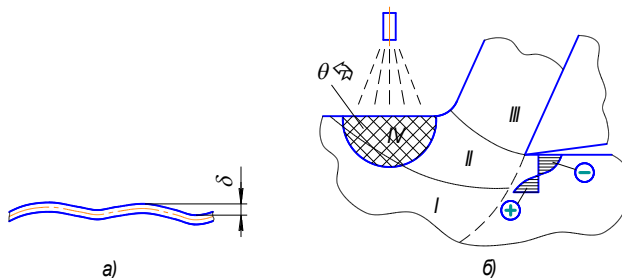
Спосіб обробки плоских нежорстких заготовок:
